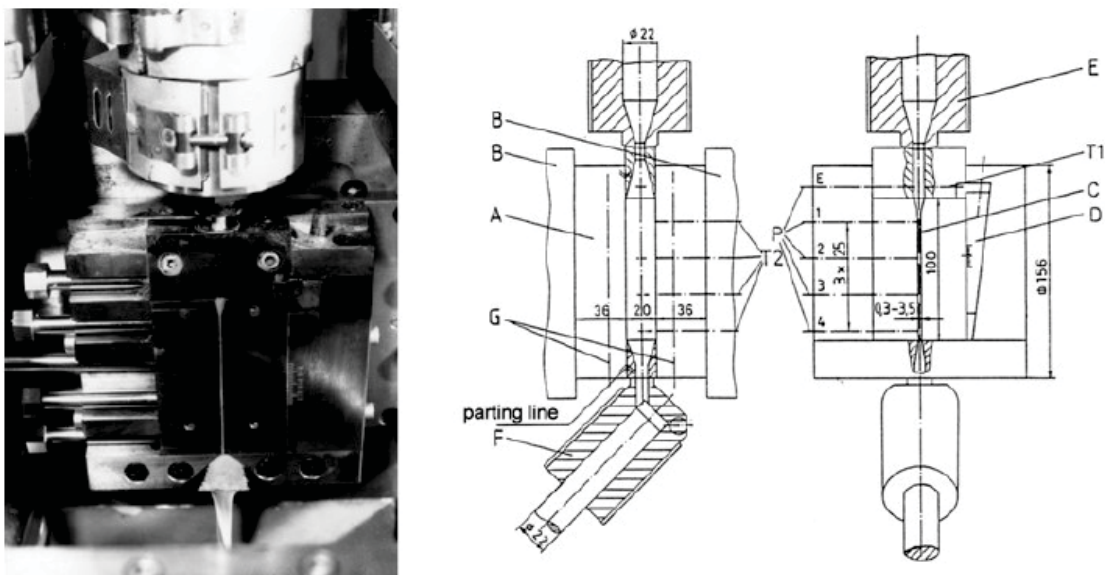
Geöffnetes in-line Spritzgießmaschinenrheometer (links) und Schnittdarstellung (rechts): A...Obere Werkzeugplatte, B...Werkzeugaufspannplatten, C...Rechteckschlitz, D...Keil, E...Spritzeinheit, F...Volumenstrommesszylinder, G...Temperierkanäle, T1 und T2...Temperaturmessung, P...Druckmessung [20].
